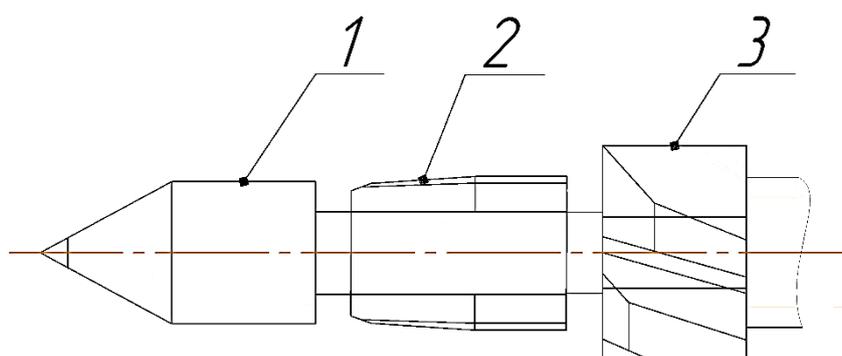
Схема конструкции комбинированного инструмента для формообразования резьбовых отверстий в заготовках из листового металла
